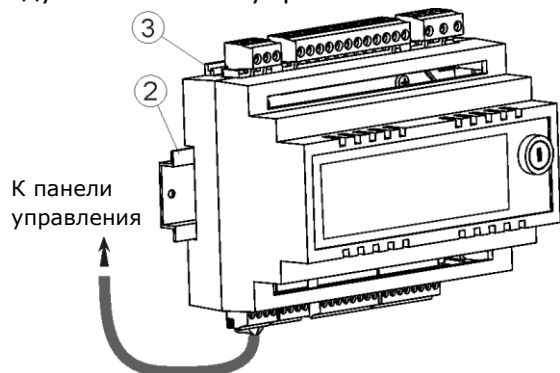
Закрепление регулятора на рейке, где: 1 - исполнительный модуль, 2 - рейка DIN TS35, 3 - крепления.
